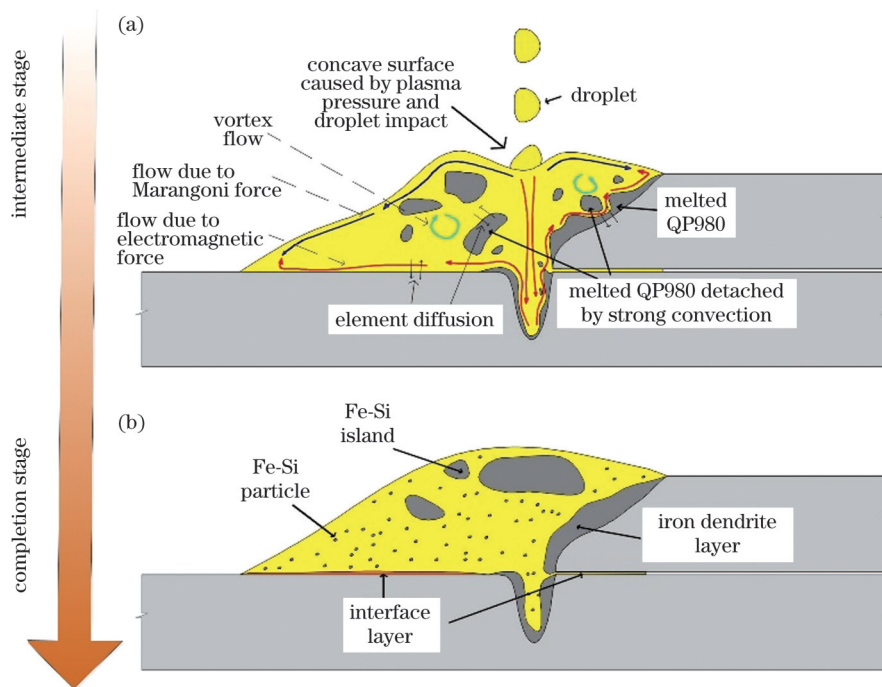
激光-TIG 复合焊接接头形成过程示意图。(a)焊接过程中；(b)焊接结束
